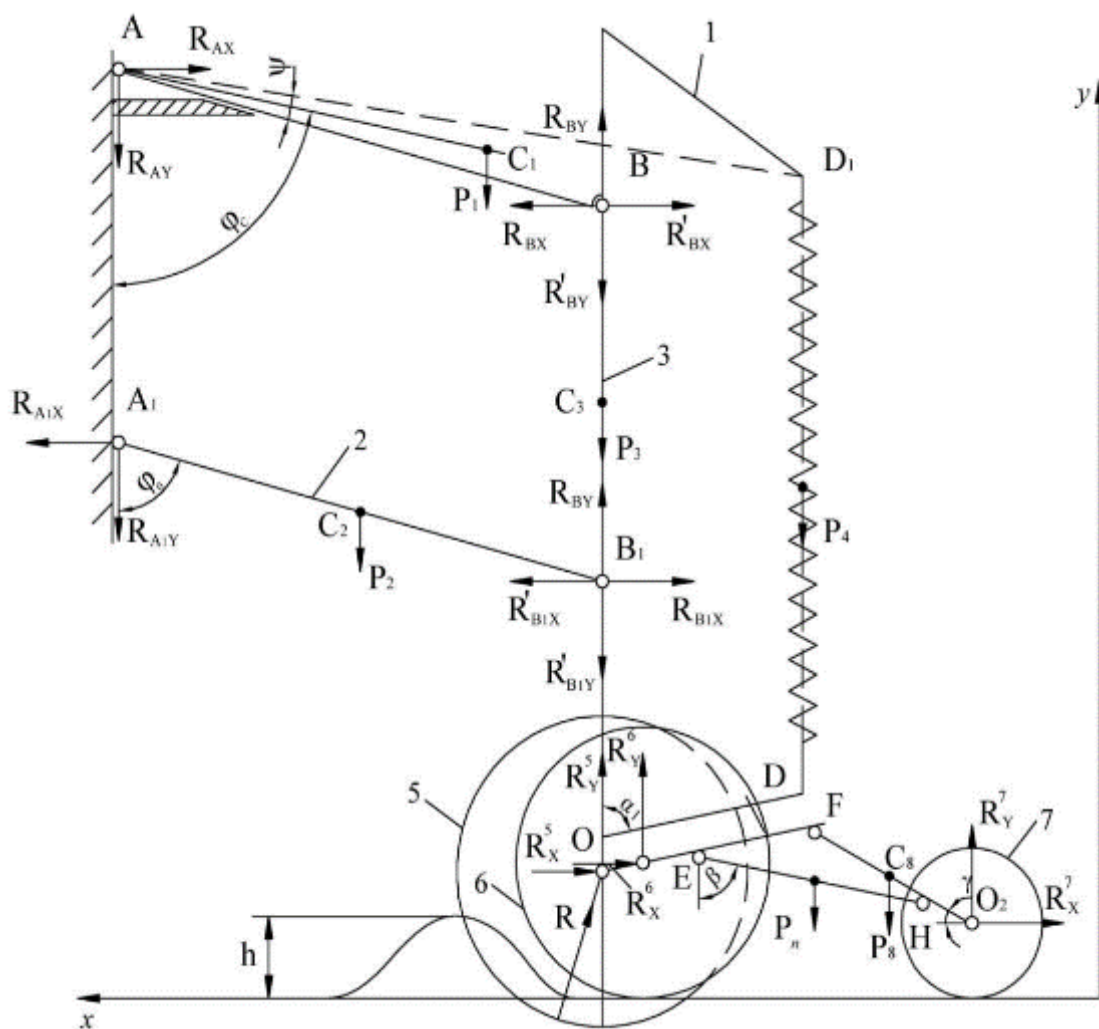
Силова картина взаємодії між елементами паралелограмного копіювального механізму: 1 – верхня тяга; 2 – нижня тяга; 3 – стійка; 4 – пружина; 5 – диск; 6 – опорне колесо; 7 – прикочуюче колесо; 8 – важіль прикочуючого колеса [10]. Розшифрування схеми в [11].
